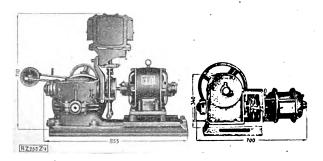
Aufzugmaschinen von gleicher Leistung. Ausführungen mit verschiebbarem Anker (rechts) und mit Bremsmagneten (links). Das Bild zeigt die Raumersparnis der neuen Ausführung.
